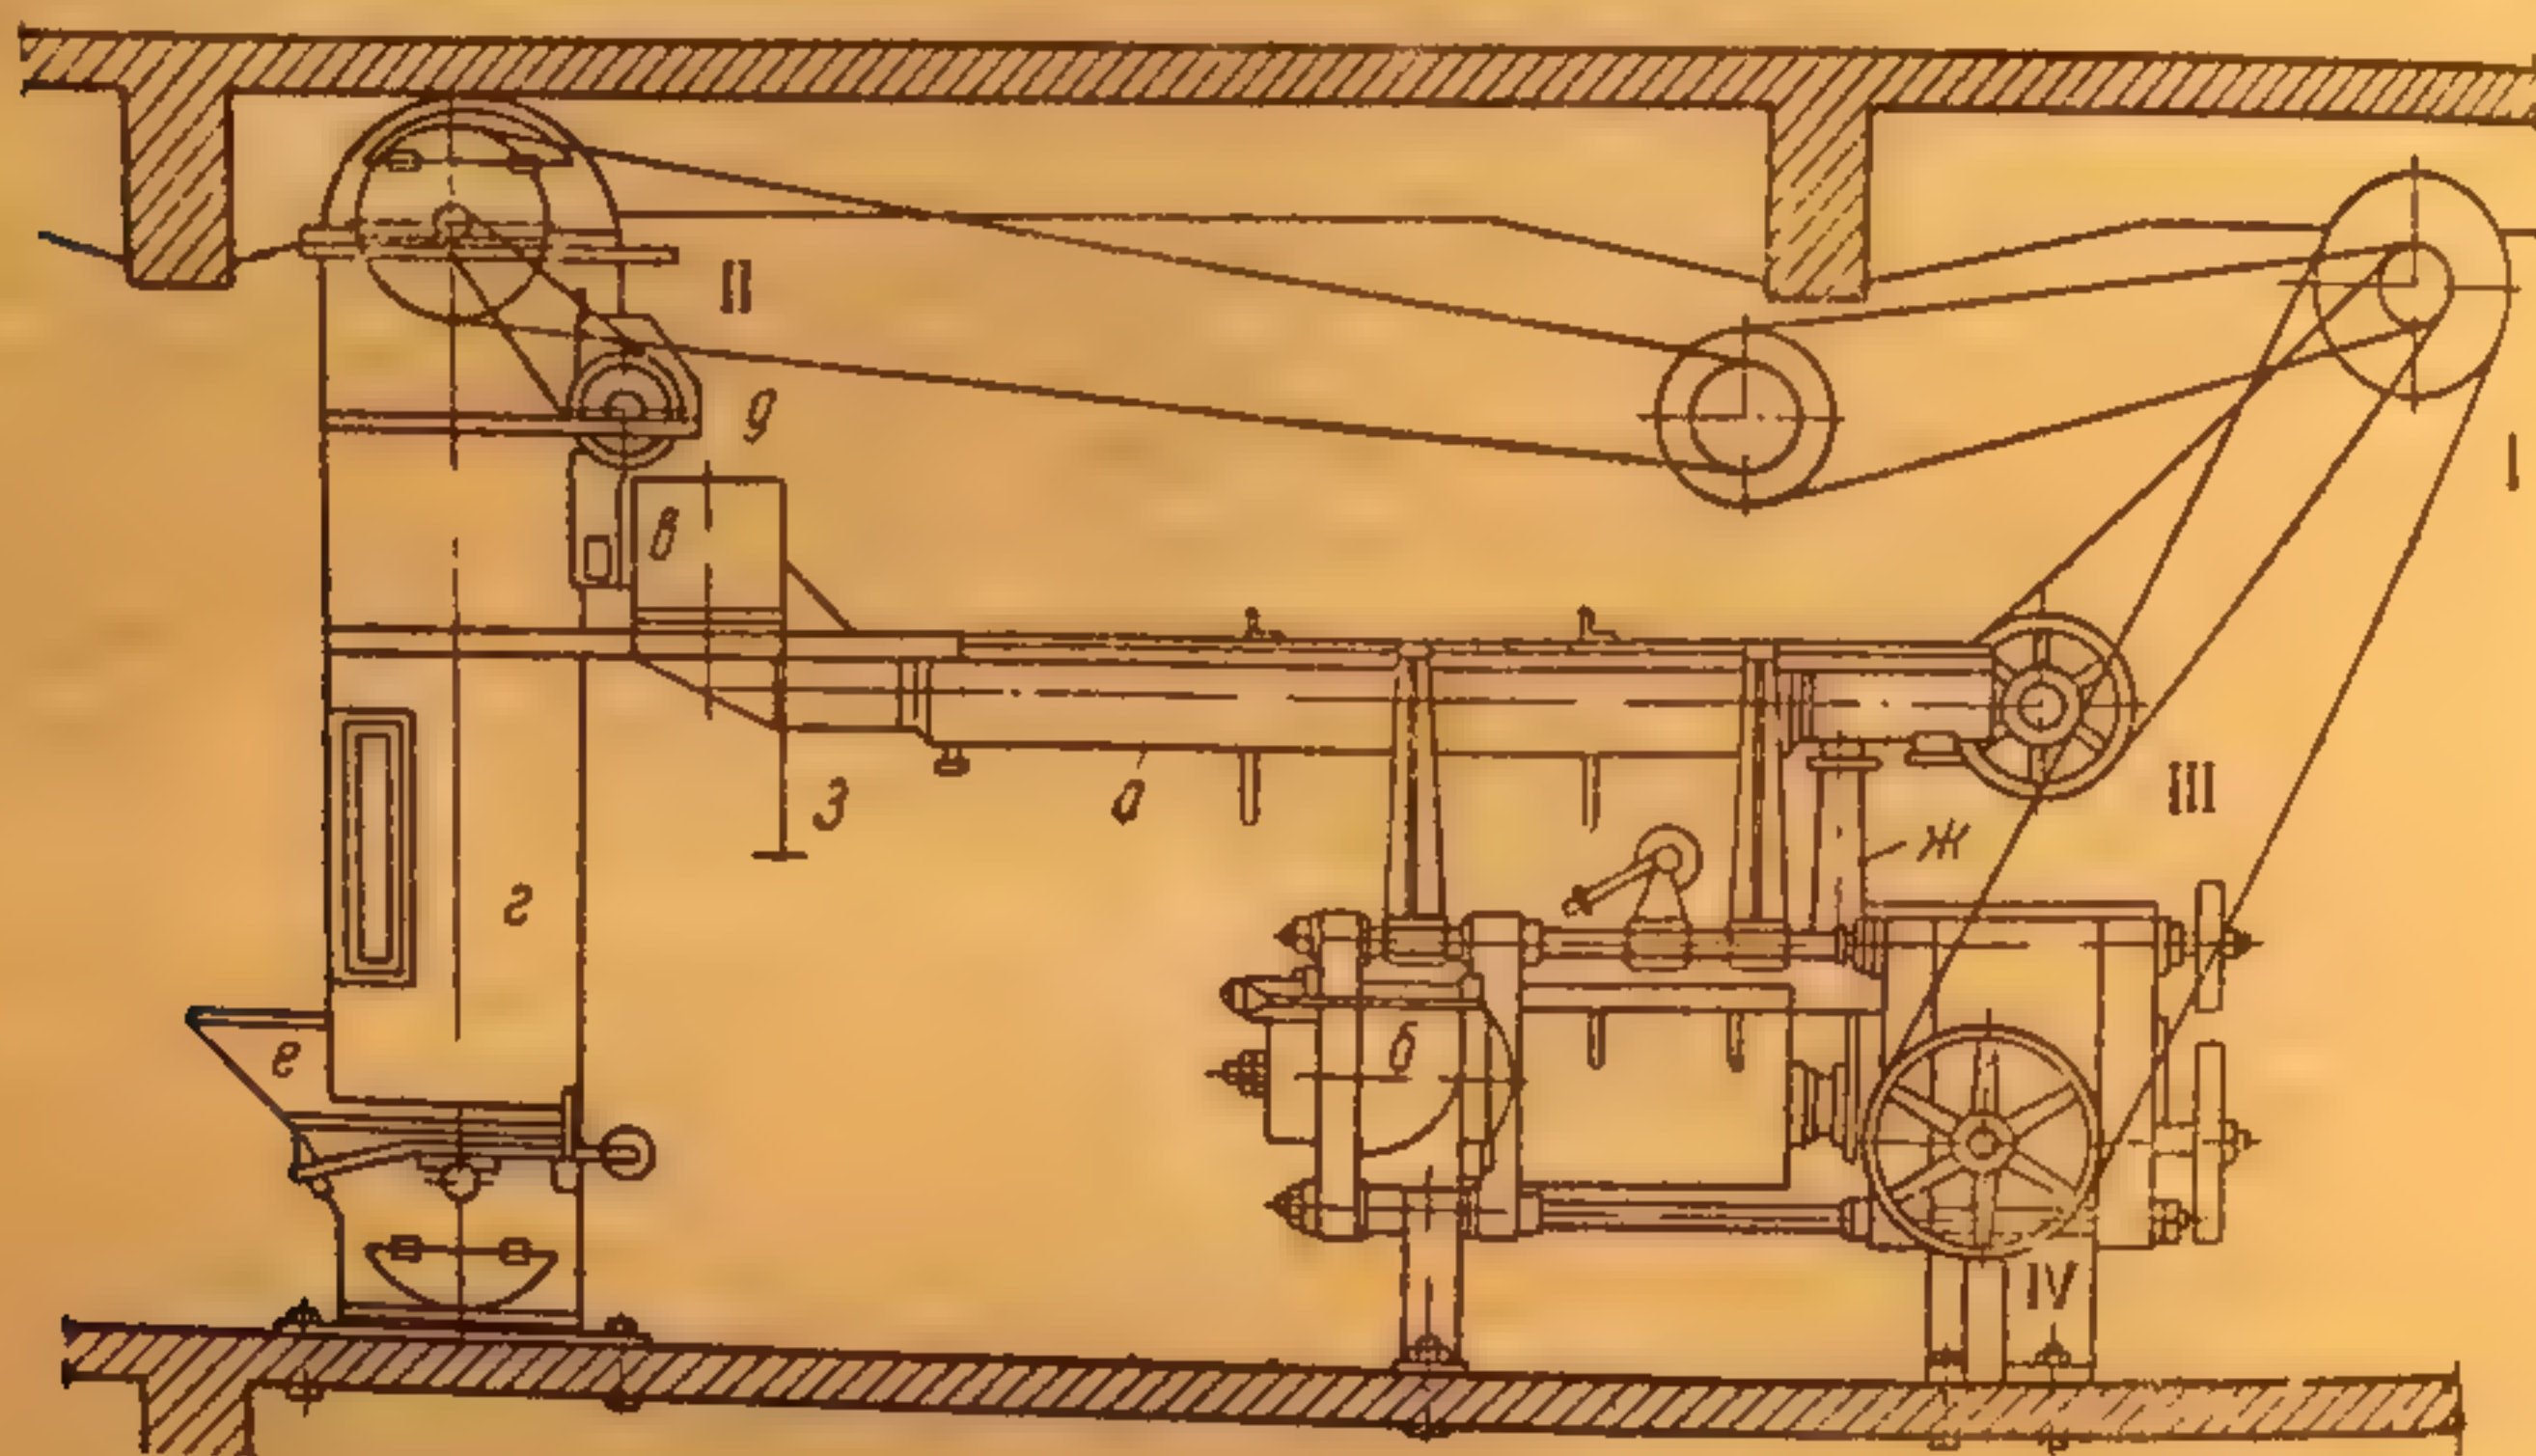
Схема общего вида установки непрерывнодействующего пресса: I — промежуточная трансмиссия, II — приводная звездочка нории, III — шкив шнека, IV — шкив пресса.
